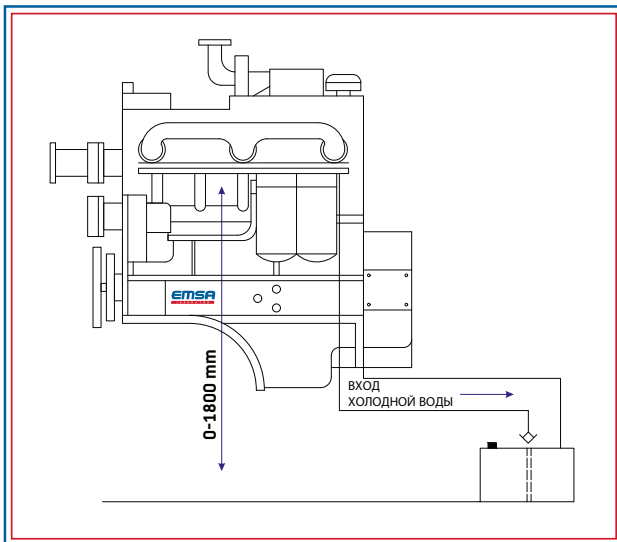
а Типичная схема топливного контура с топливным баком ниже двигателя
